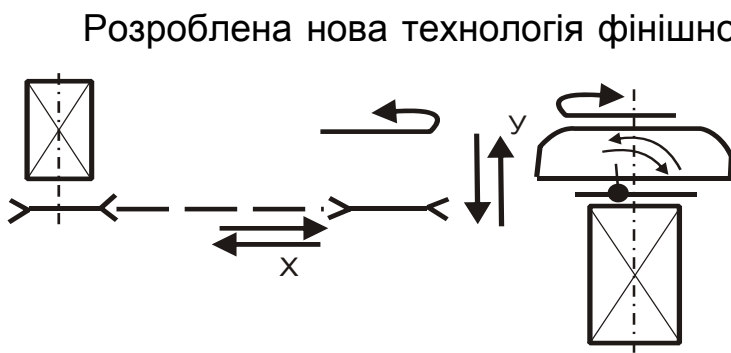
Схема руху інструмента й деталі в процесі обробки зовнішньої поверхні
